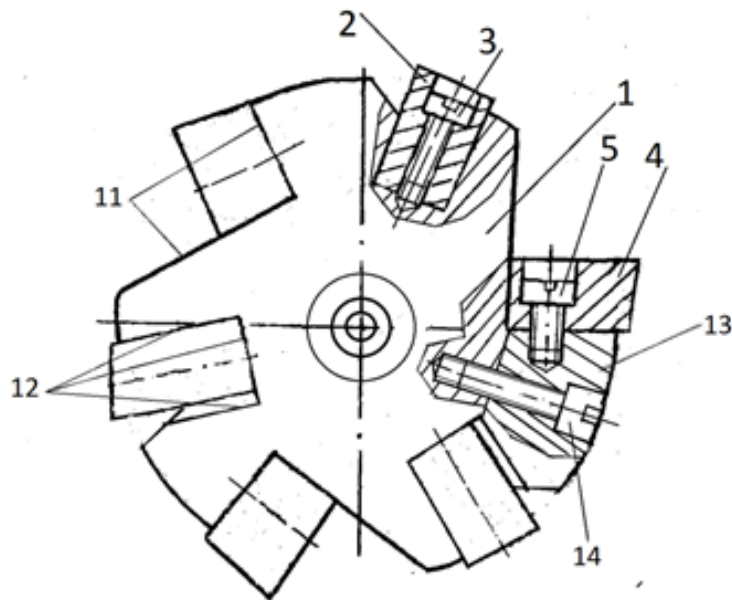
Вид торцово-цилиндрической фрезы со стороны торцовой части, имеющей комбинированное крепление радиальных и тангенциальных режущих пластин со сменными промежуточными деталями для крепления радиальных пластин
